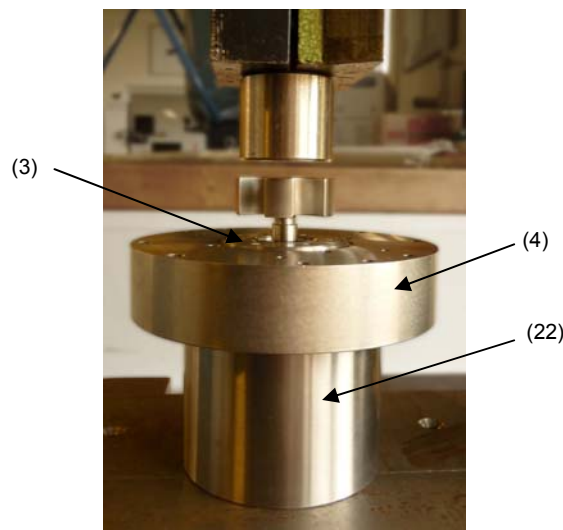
Montagehilfe zum Pressen der Rotoren
